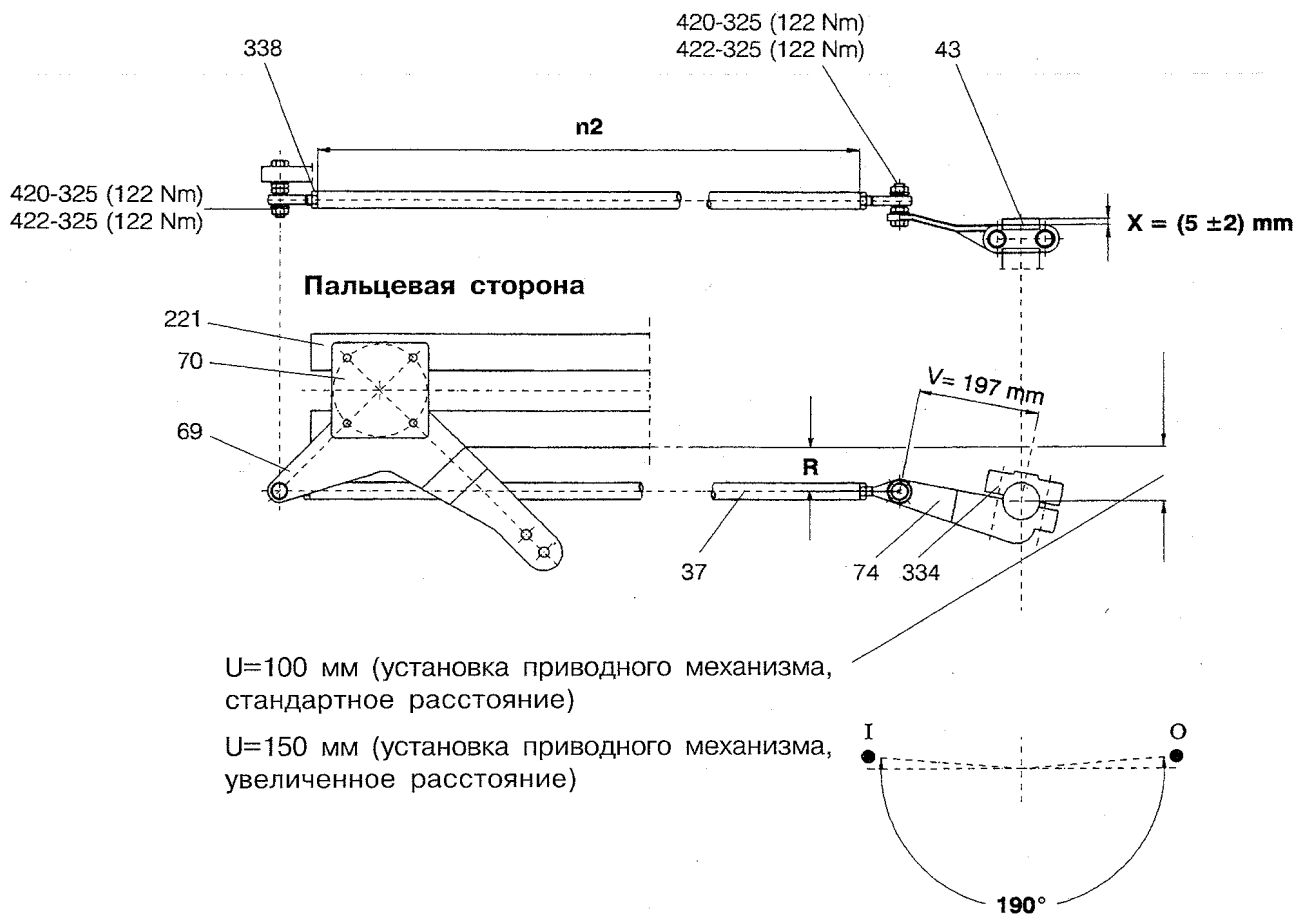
Установка тяг разъединителя: регулировка приводного механизма разъединителя при расположении приводного механизма разъединителя на стороне противоположной открывания
